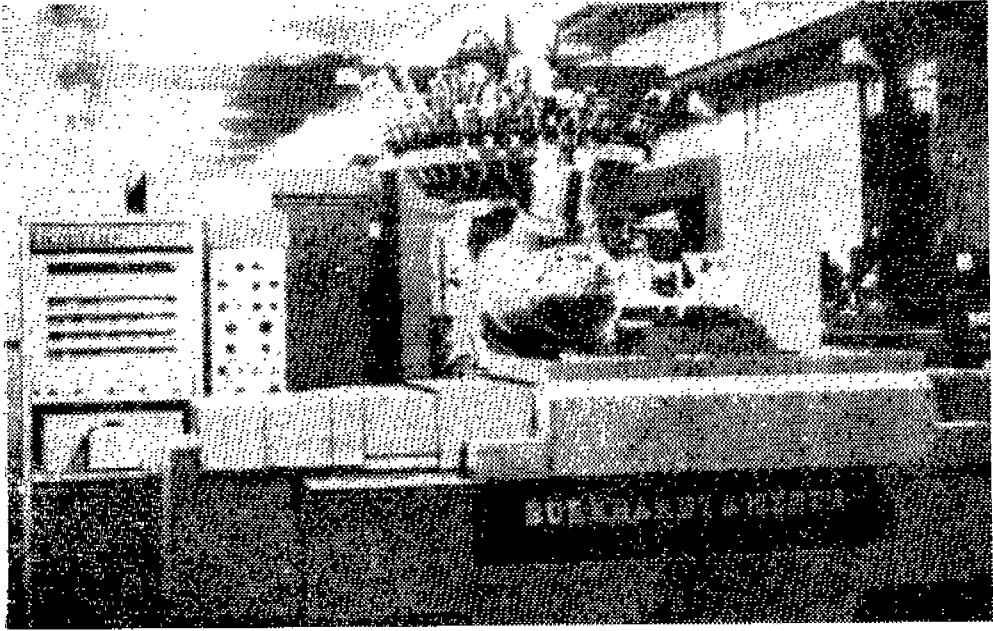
Siemens 베르린 차단기類 공장에 설치된 Sinumerik 직선절삭제어가 장치된 machining centre : MC20A(maker : Burkhardt and weber Co.)
